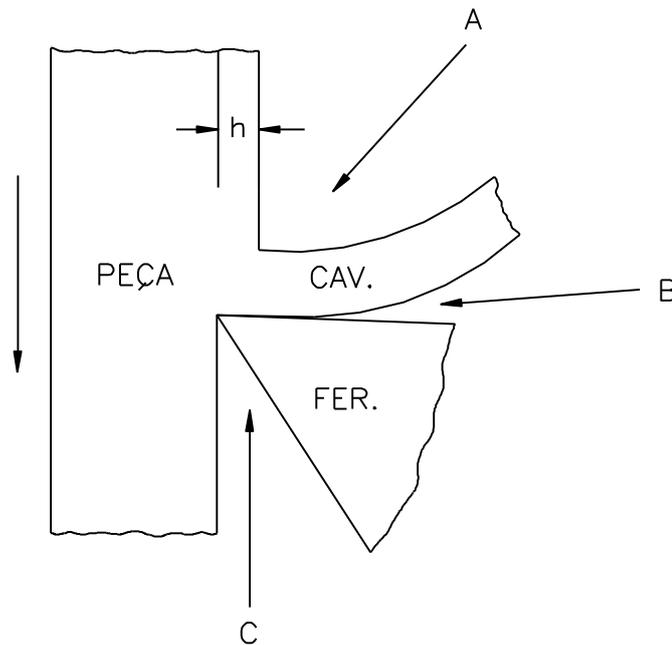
As três direções possíveis (A = sobre a cabeça; B = entre a superfície inferior do cavaco e a superfície de saída da ferramenta; C = entre a peça e a superfície de folga da ferramenta) Fonte: (Barbosa, 2009)
